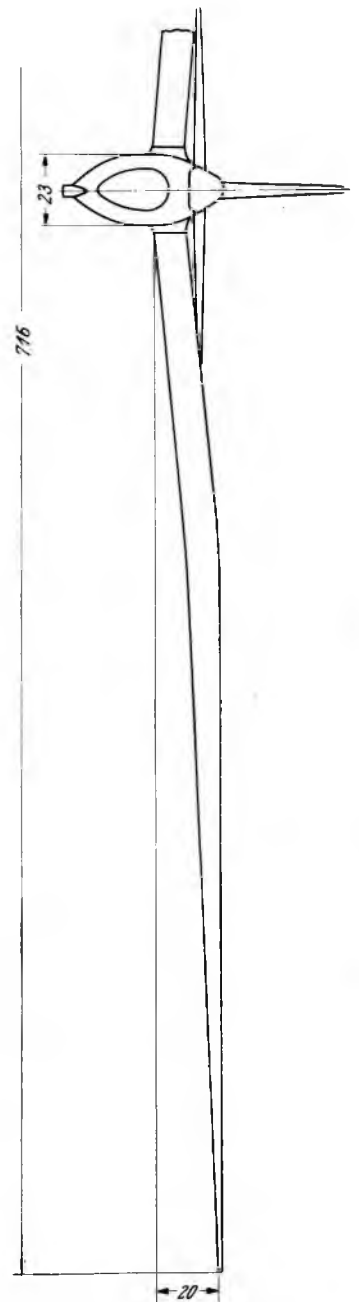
Kernholzbrettchen zum Bau des „Kranich“.
